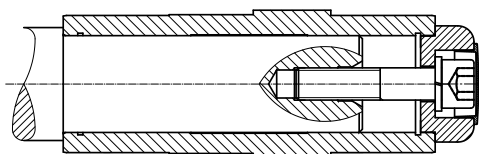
Крепление редуктора к валу с упором с помощью крепежного узла
